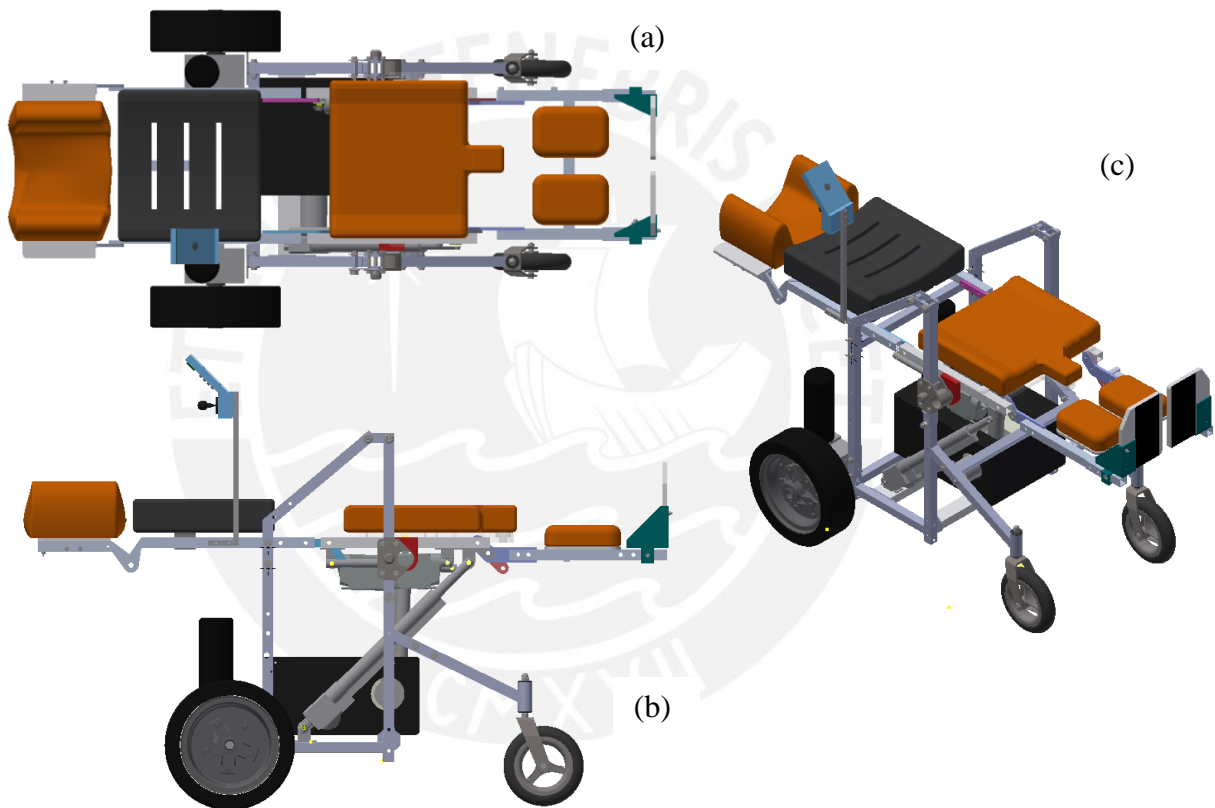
Función camilla - - (a) Vista superior (b) Vista frontal
